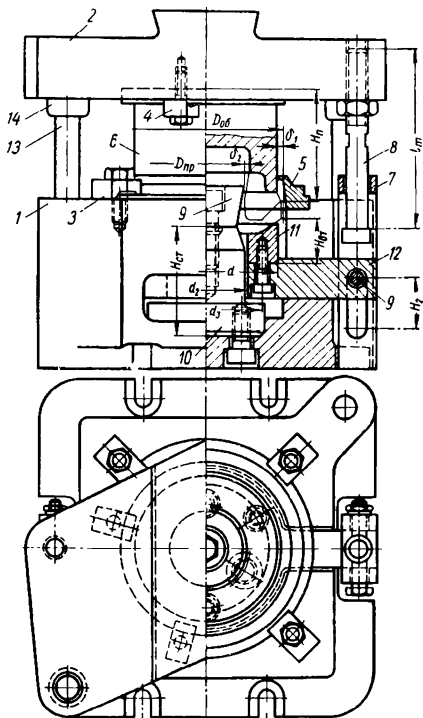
Типовой совмещенный штамп для обрезки-прошивки поковок круглой или близкой к ней формы: 1, 2 — плиты нижняя и верхняя; 3, 4 — захваты нижний и верхний; 5 — матрица; 6 — пуансон; 7 — скоба; 8 — тяга; 9 — прошивник; 10 — стойка прошивника; 11 — выталкиватель; 12 — коромысло выталкивателя; 13 — колонка; 14 — втулка — направляющие
